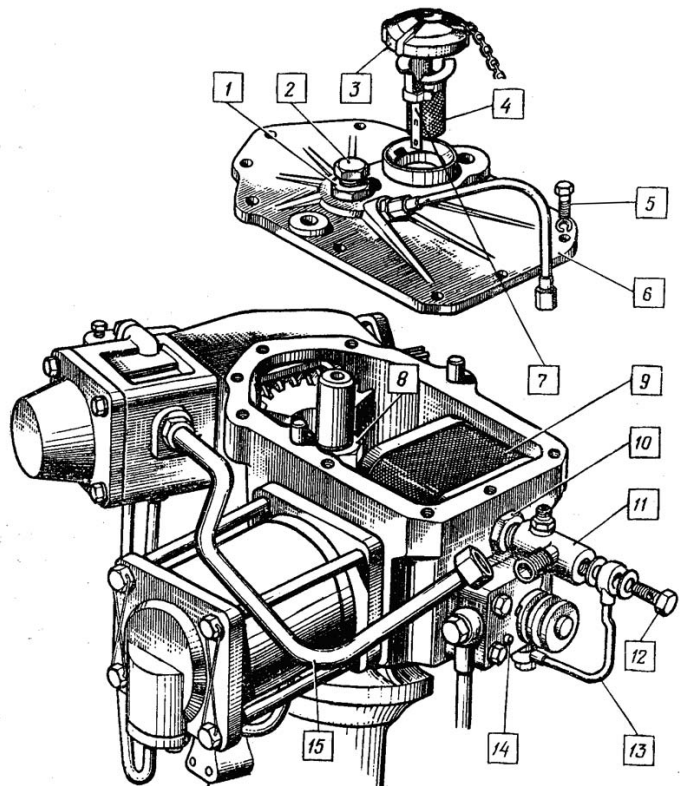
Гидроусилитель рулевого управления: 1, 10 — контргайки; 2 — регулировочный болт; 3 — крышка заливной горловины; 4 — фильтр; 5, 12 — болт; 6 — крышка; 7 — масломер; 8 — гайка; 9 — сливной фильтр; 11 — клапан; 13 — маслопровод клапана; 14 — шуп; 15, 16 — маслопроводы.
